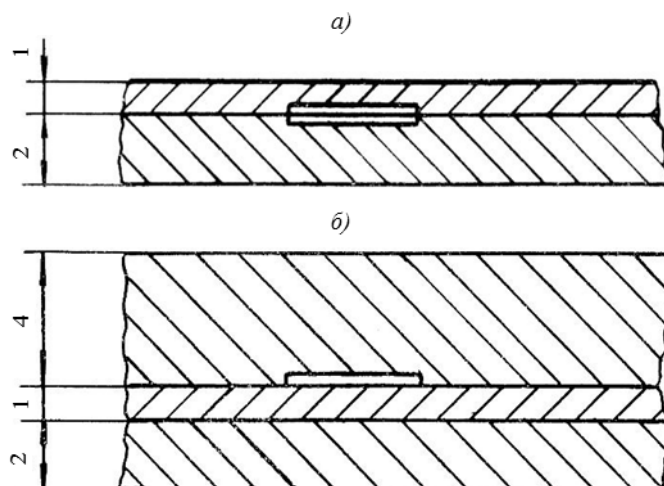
Образцы двухслойной (а) и трехслойной (б) конструкции с искусственными дефектами
